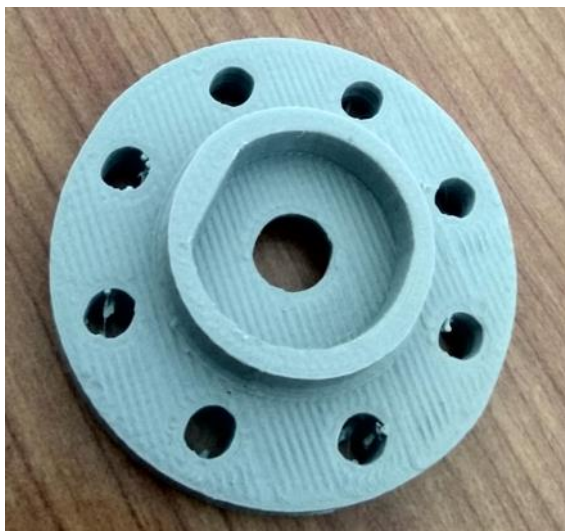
Impressão 3D flange acoplamento ao sensor
